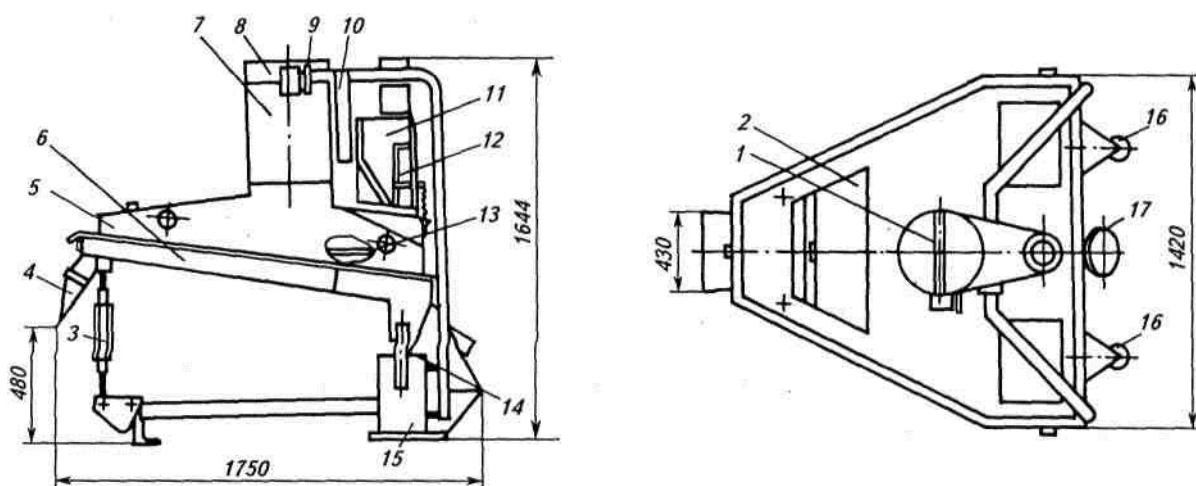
Камнеотделительная машина У12-БКТ-100: 1 — регулировочный клапан; 2 — заменяемая дека; 3 — механизм регулировки; 4, 8, 16 — патрубки; 5 — корпус; 6 — рама; 7 — гибкий рукав; 9 — маховик; 10 — манометр; 11 — приемник; 12 — запорный клапан; 13 — распределитель; 14 — пружина; 15 — неподвижная рама; 17 — привод.
